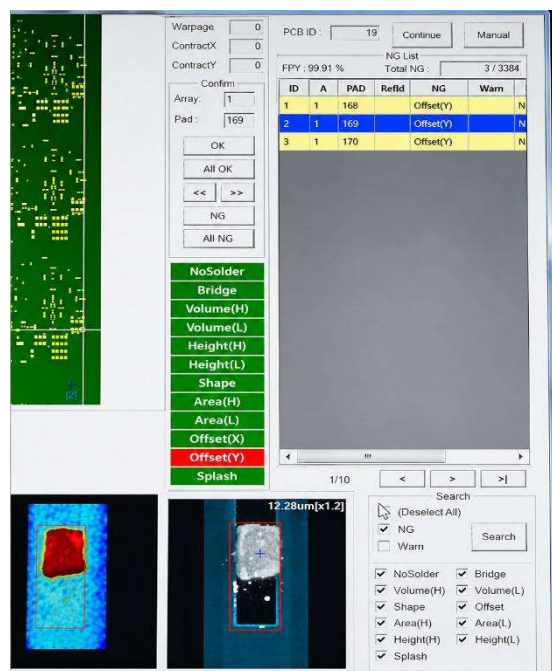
Insuficiencia de soldadura detectada en SPI.
